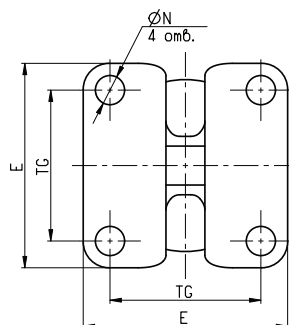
Пневмоцилиндр 91 серии в сборе с шарнирным креплением LSJ-91
